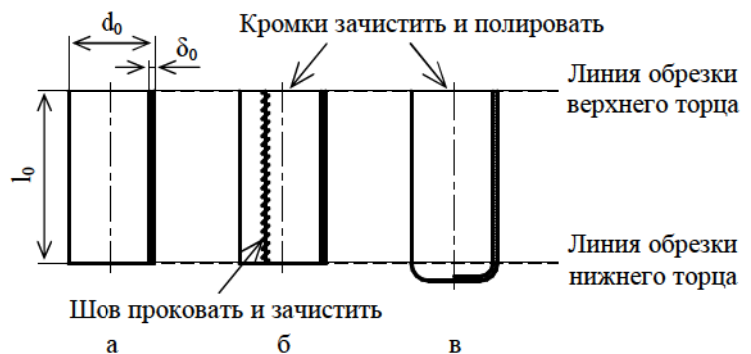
Варианты заготовок из различных полуфабрикатов: а – цельнотянутая труба; б – сварная труба; в – стаканчик, полученный вытяжкой из листа
